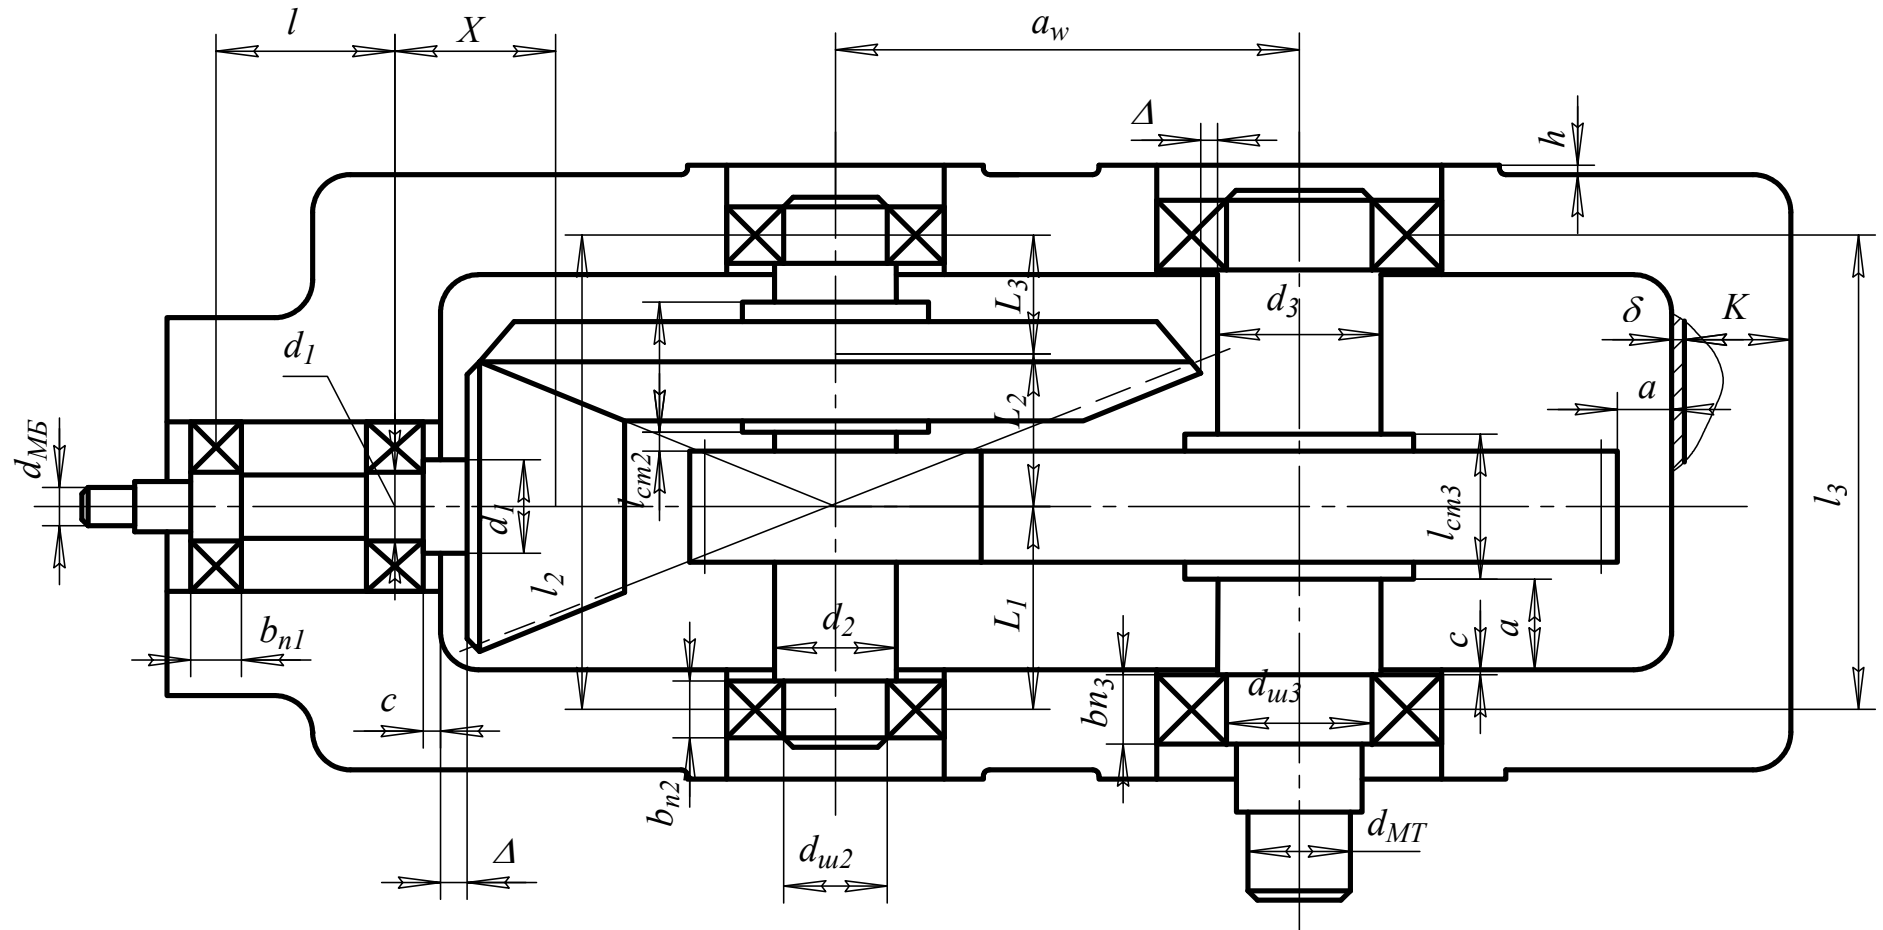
Ескізне компоунвання двохступеневого конічно-циліндричного редуктора
